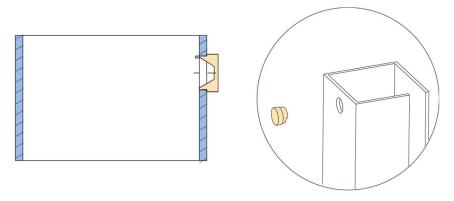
Croquis detalles montaje tapón de bloqueo
